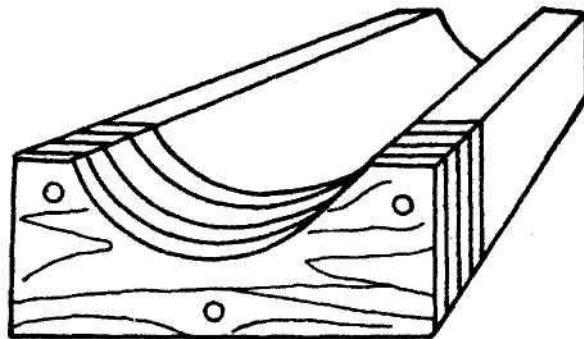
Схема блока з клеєної деревини для виготовлення дерев'яної прес-форми
